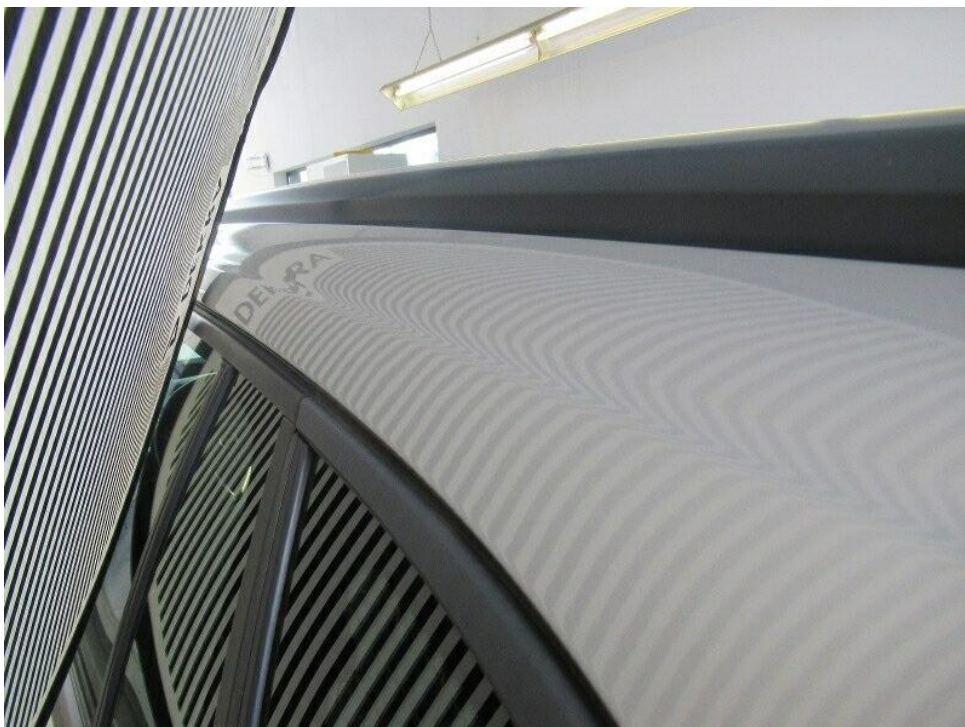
Dachrahmen links, eingedellt, Gebrauchsspur
